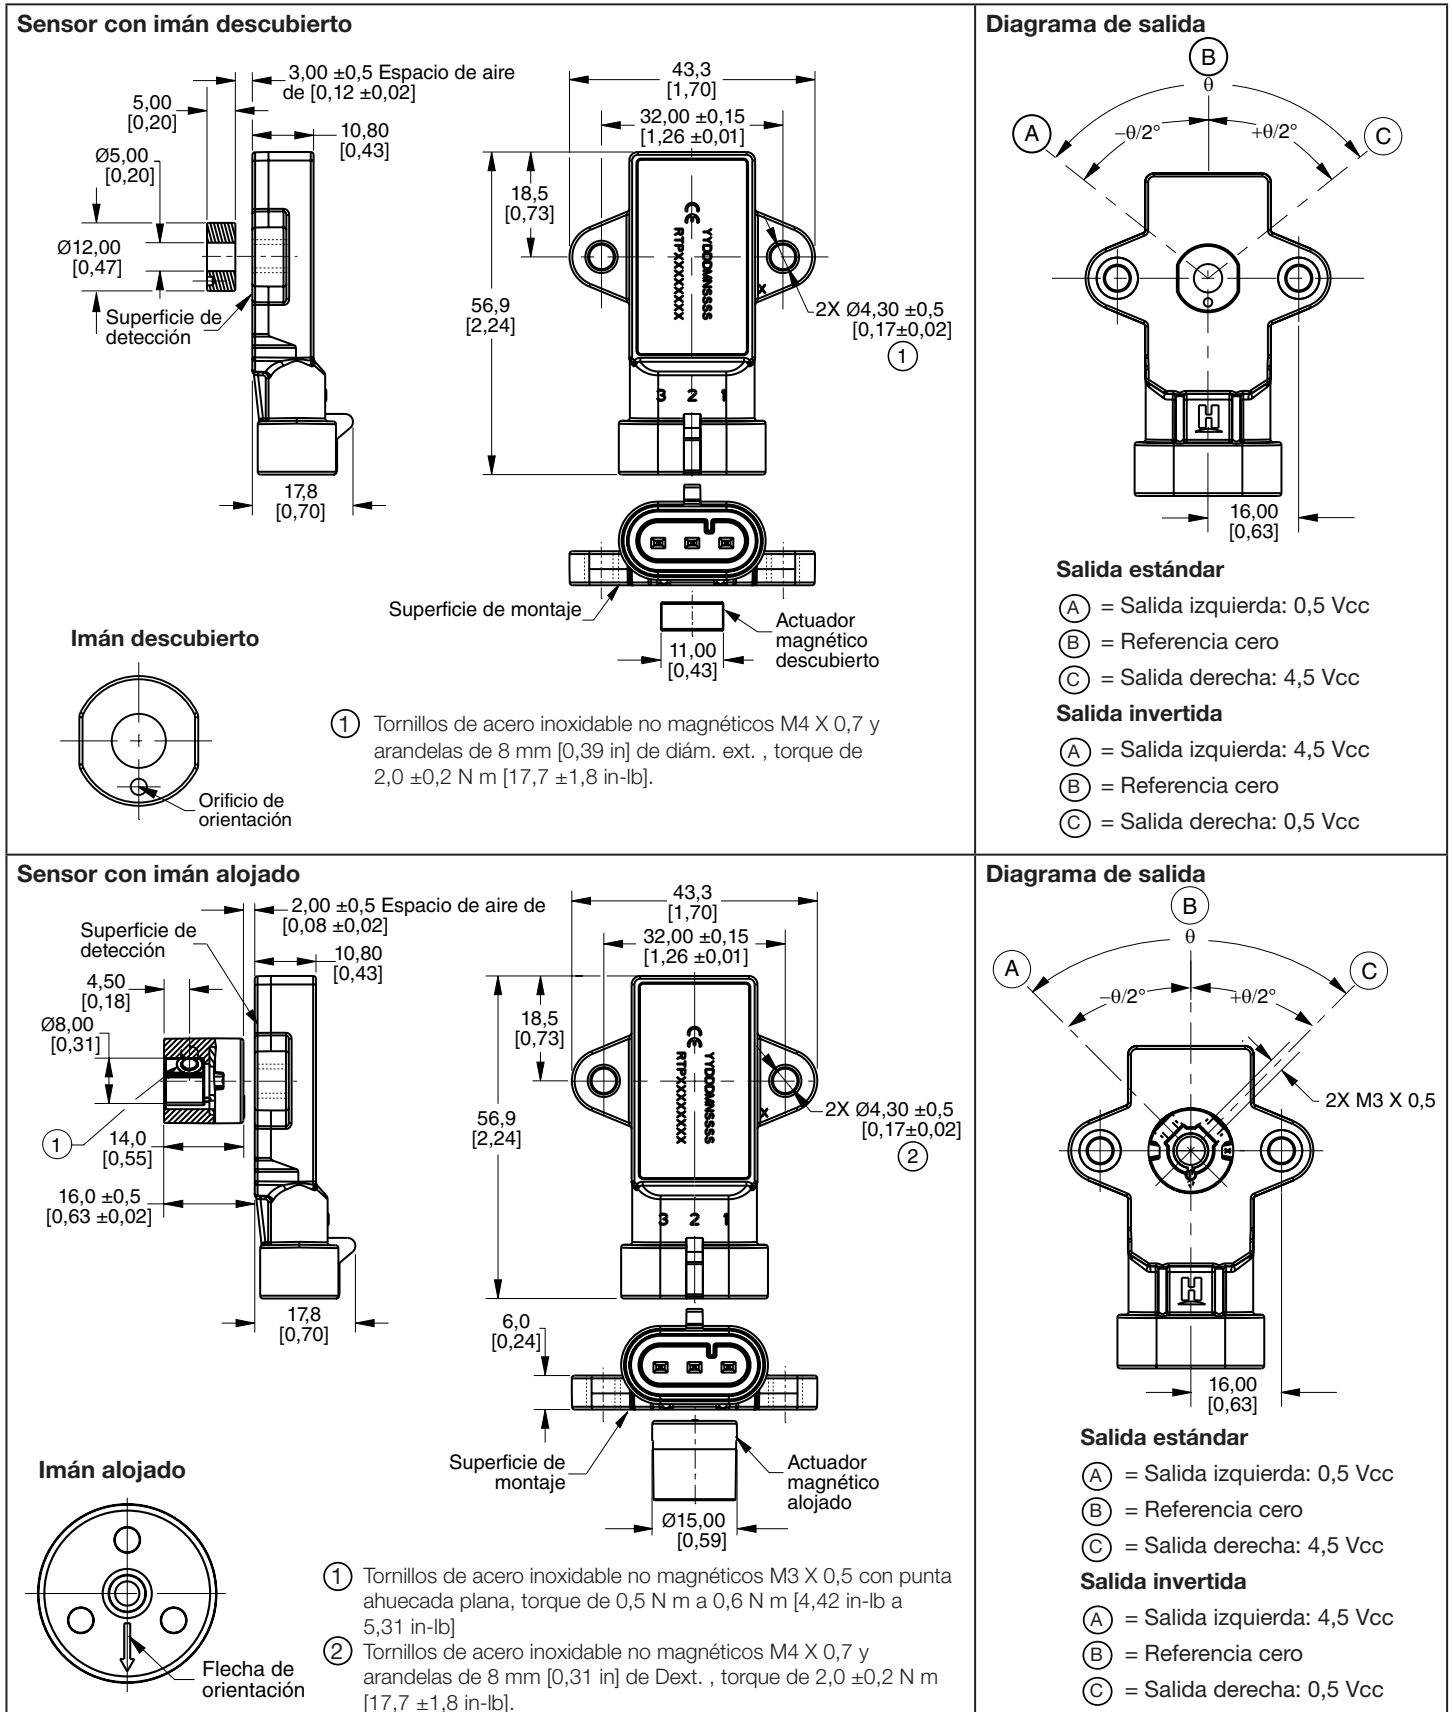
Información de montaje del actuador magnético alojado y sensor (solo para consulta) in/[mm].
